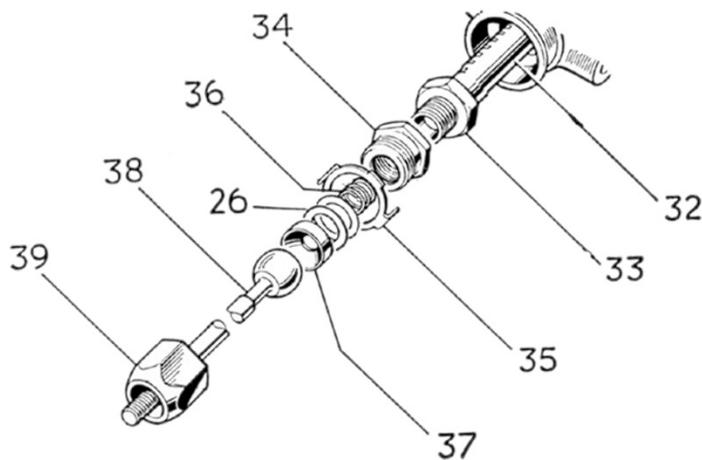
Joint à rotule intérieur de la barre d'accouplement
